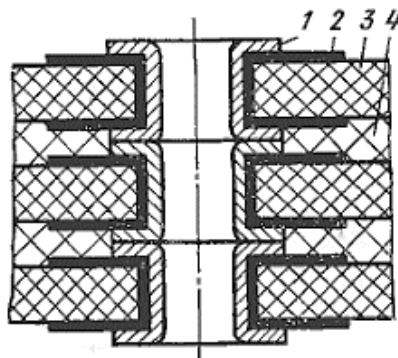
З'єднання по фланцям, що дотинаються: 1 – об'ємна деталь чи пістон; 2 – припой; 3 – основа; 4 – проміжний шар.
